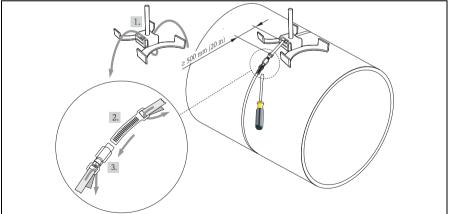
Prémontage des colliers de serrage pour diamètres de conduite DN > 600 (24")
